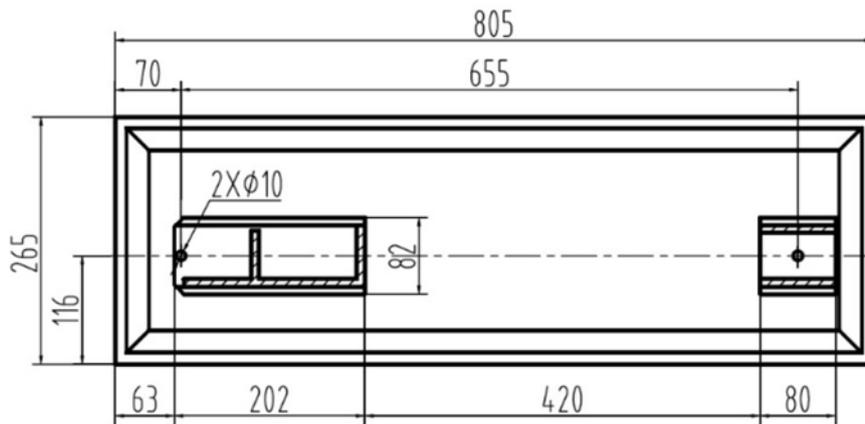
Schema der Drehmaschinenbett-Ankerschraubenbohrungen
